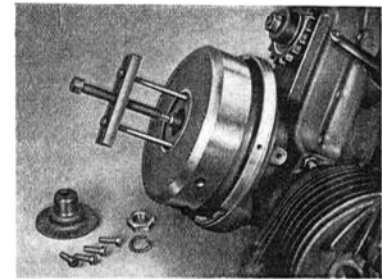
Abziehen des Glockenankers mit Abzieher Nr. 0100031. Beide Zugschrauben ganz einschrauben! Besser Abzieher Nr. 0100033 verwenden (s. Bild 211)
